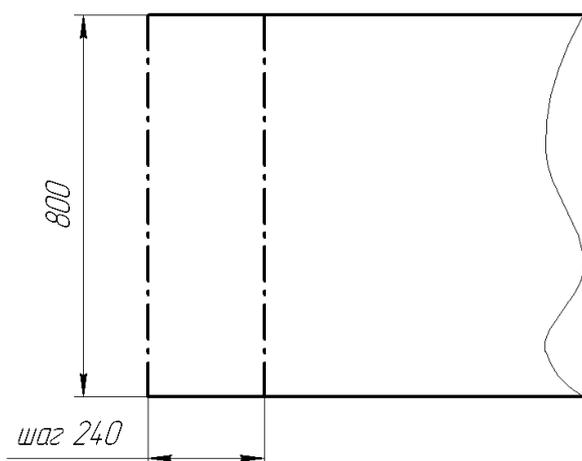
Раскрой и размеры заготовок в существующем варианте
